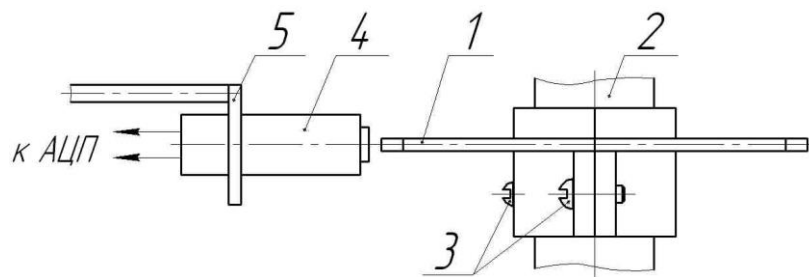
Схема установки тахометрического датчика (вид сверху):
